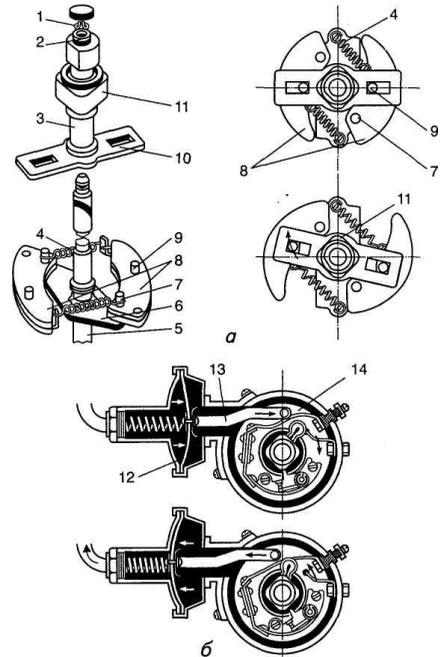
Регулятори випередження запалювання: а – відцентровий; б – вакуумний; 1 – замкове кільце; 2 – опорна шайба; 3 – втулка кулачка; 4 – пружина; 5 – вал приводе; 6 – пластина; 7 – вісь; 8 – тягарці; 9 – штифт; 10 – планка; 11 – кулачок переривника; 12 – діафрагма; 13 – тяга; 14 – рухомий диск переривника
